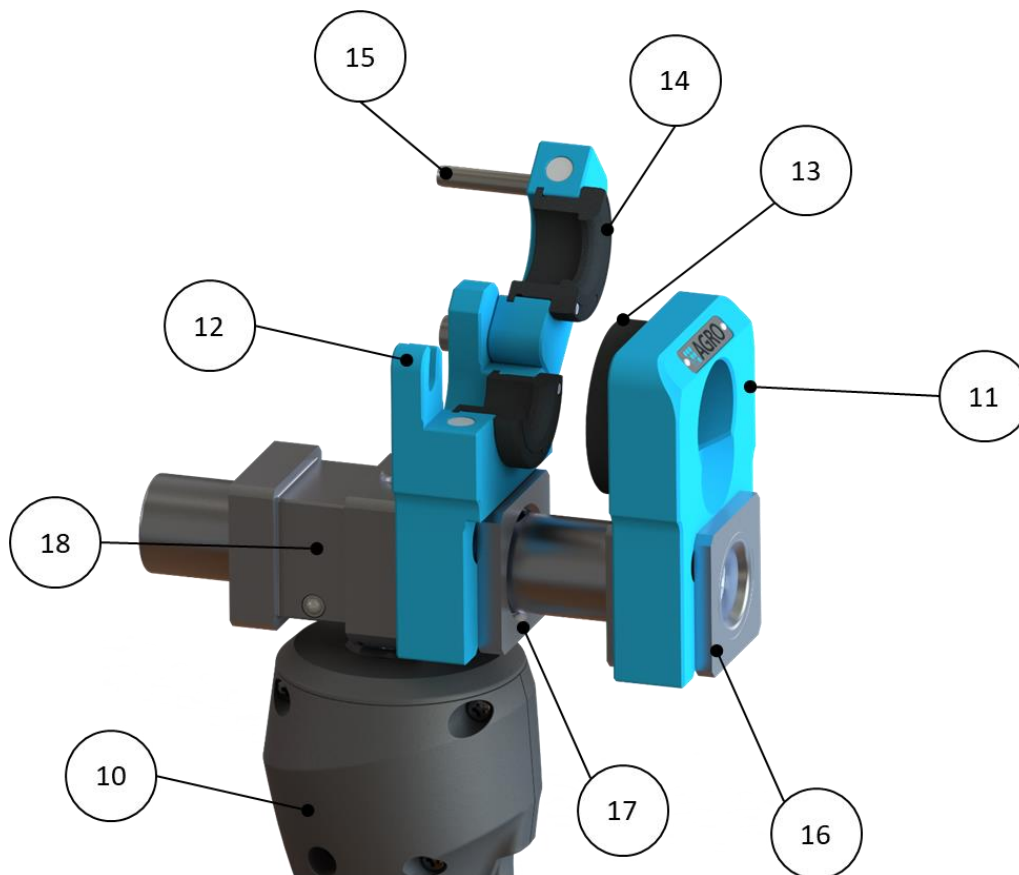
Rappresentazione dell'utensile di assemblaggio con attrezzo di serraggio e flangiatura, così come i relativi inserti, montati
